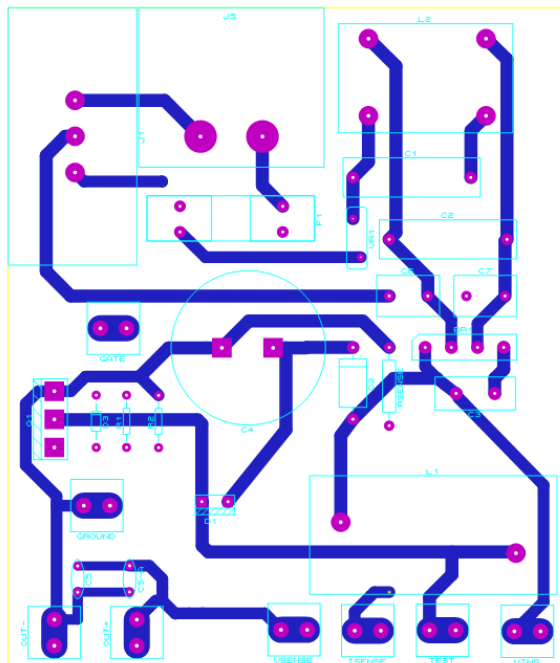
Cara posterior del PCB de circuito de fuerza, prototipo final.
